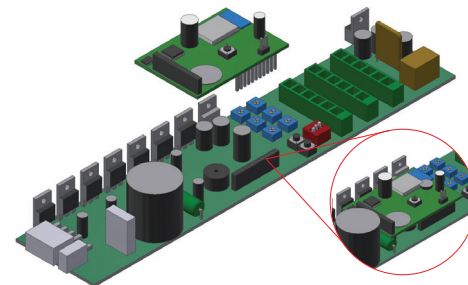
Conexão do módulo RF à placa de acesso remoto wifi slider
